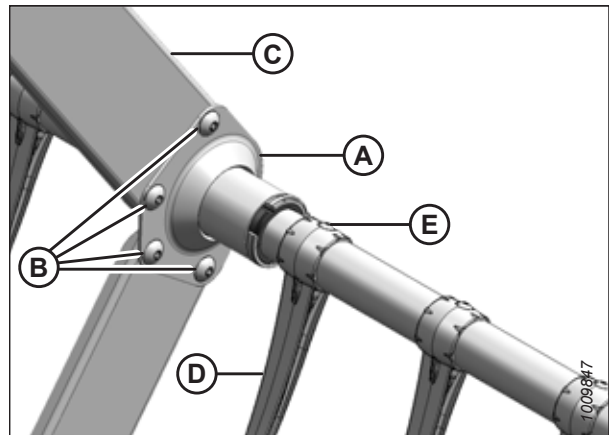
Support du kit de renforcement des tubes à doigts en option
